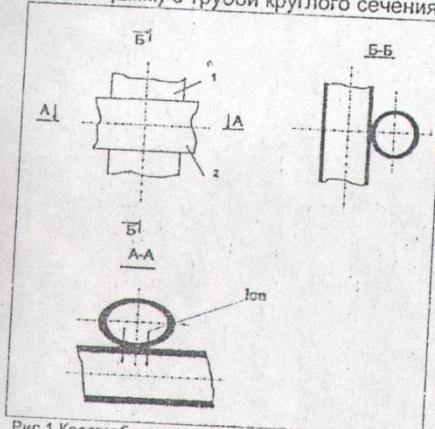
Крестообразное соединение:1-труба плоскоовального сечения;2-труба круглого сечения.
